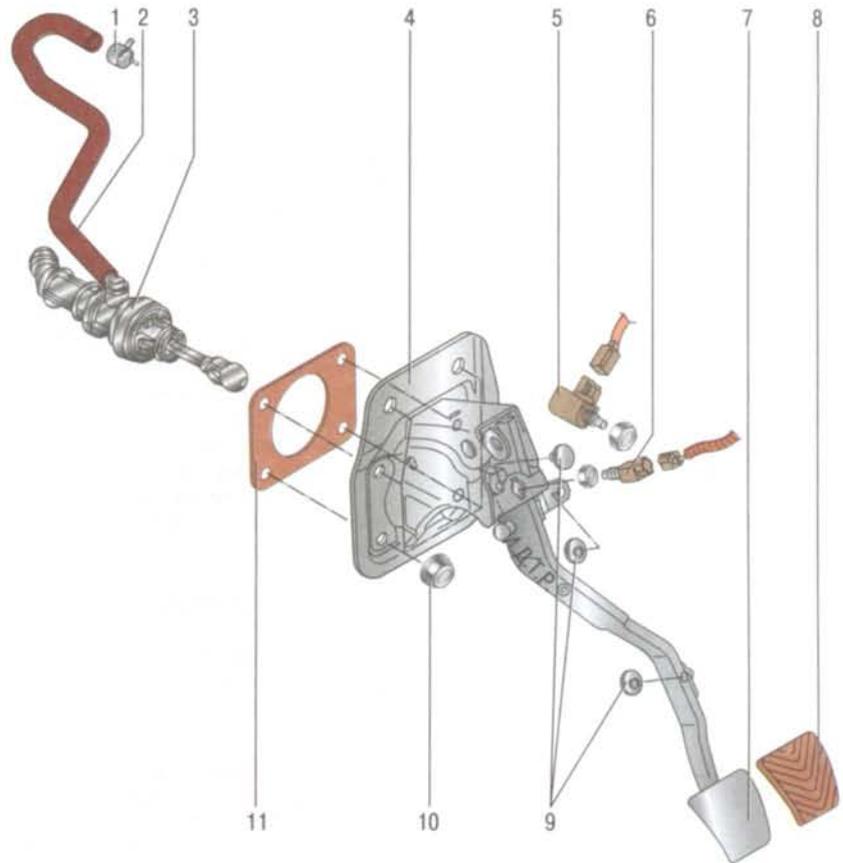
Педаль и главный цилиндр гидропривода выключения сцепления: 1 – хомут крепления шланга подачи тормозной жидкости к главному тормозному цилиндру; 2 – шланг подачи тормозной жидкости к главному тормозному цилиндру от бачка; 3 – главный цилиндр привода выключения сцепления; 4 – кронштейн педали сцепления; 5 – датчик выключения сцепления; 6 – выключатель круиз-контроля; 7 – педаль сцепления; 8 – накладка педали сцепления; 9 – упоры; 10 – гайка крепления кронштейна педали сцепления; 11 – прокладка
